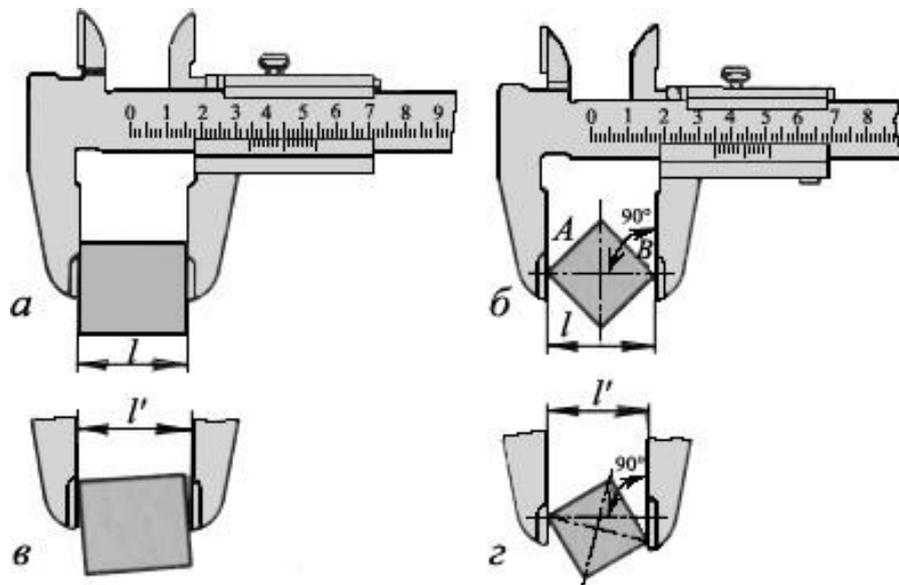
Прийоми вимірювання штангенциркулем: а, б — правильні; в, г — неправильні
